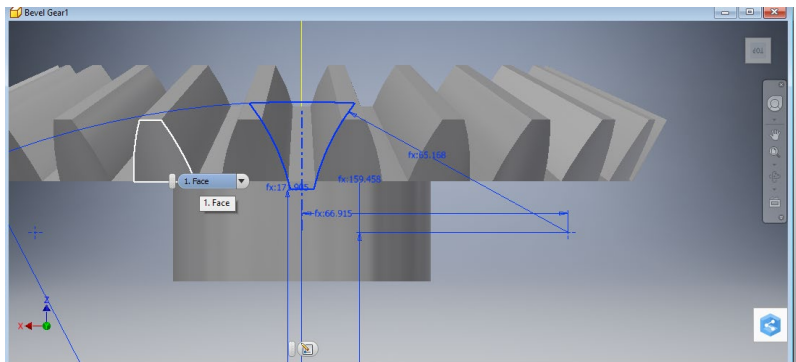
16 Hasil Keluaran Bevel Gear Standard Inventor
